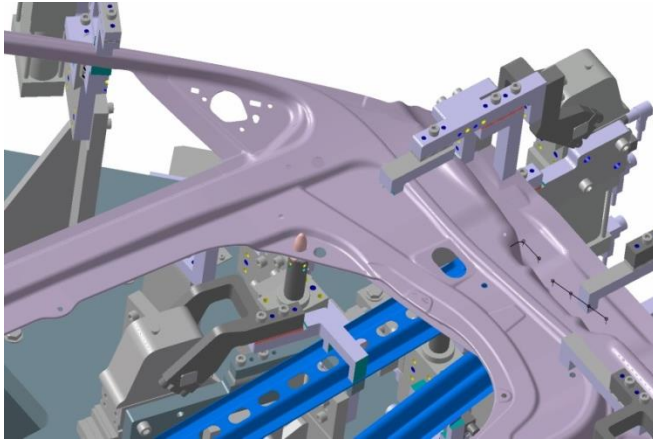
Ausschnitt der Spanntechnik beim Widerstandspunktschweißen am Beispiel der Türverstärkungen
